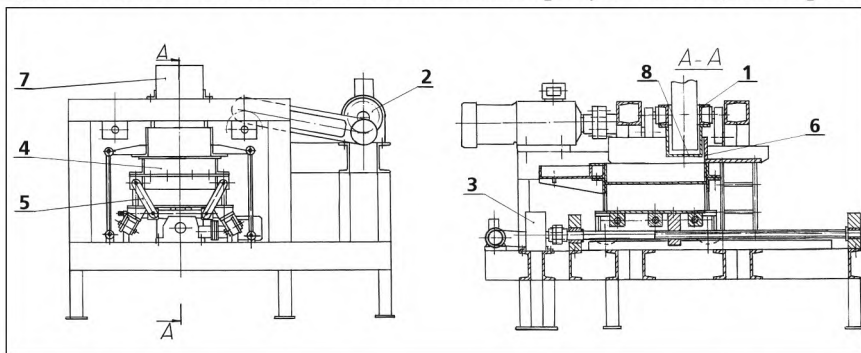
Общий вид формовочной установки зонного нагнетания: 1 - рабочий орган или нагнетатель, 2 - привод нагнетателя, 3 - механизм передвижения формы, 4 - двоянная форма, 5 - механизм распахивки формы, 6 - стабилизирующая балка, 7 - расходный бункер, 8 - нагнетающая гребёнка.
